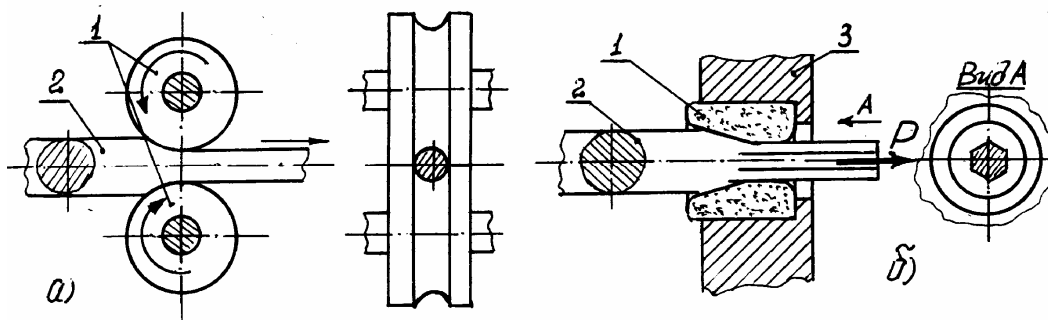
Схемы обработки металлов прокаткой (а) и волочением (б).
